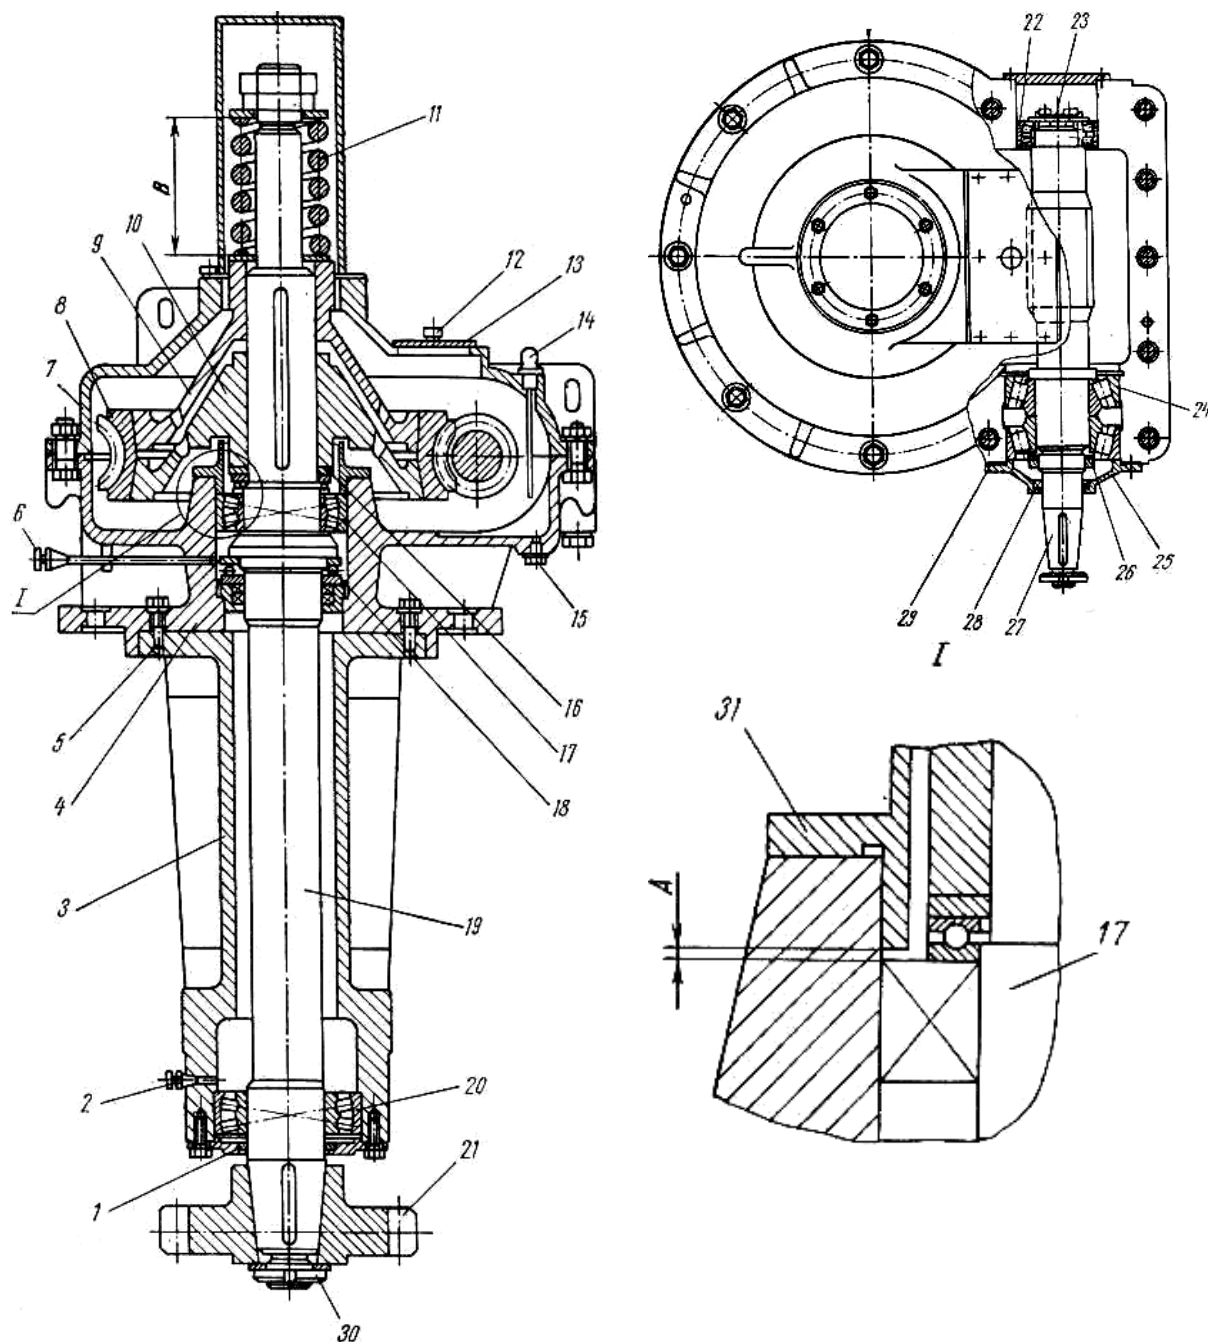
Червячный редуктор механизма поворота с муфтой предельного момента:
